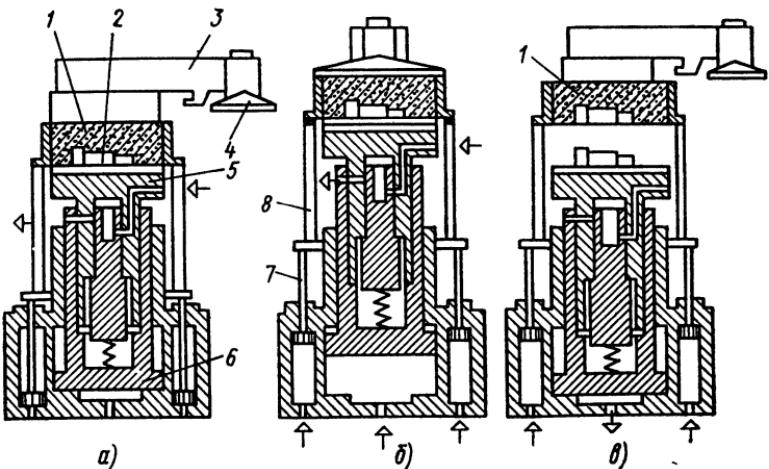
Схема изготовления верхней полуформы на встряхивающейся прессовой машине модели 22111 со штифтовым съемом:
